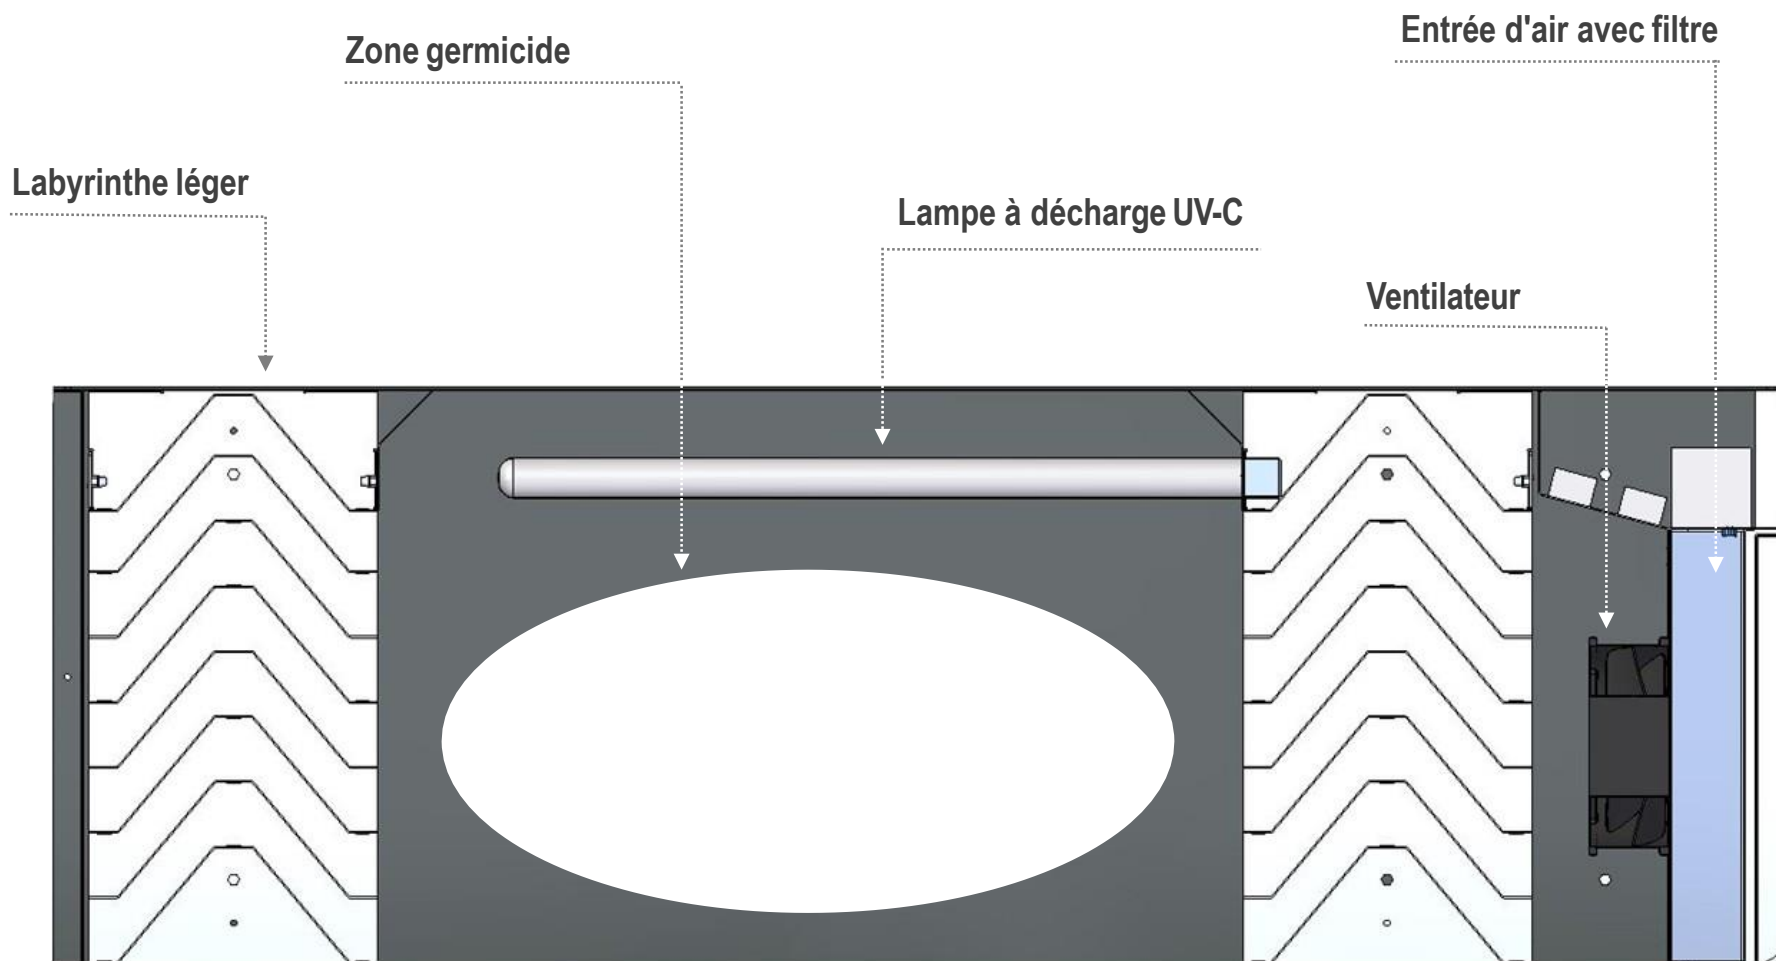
DETAILS TECHNIQUES AC 20 VUE LATÉRALE AVANT
